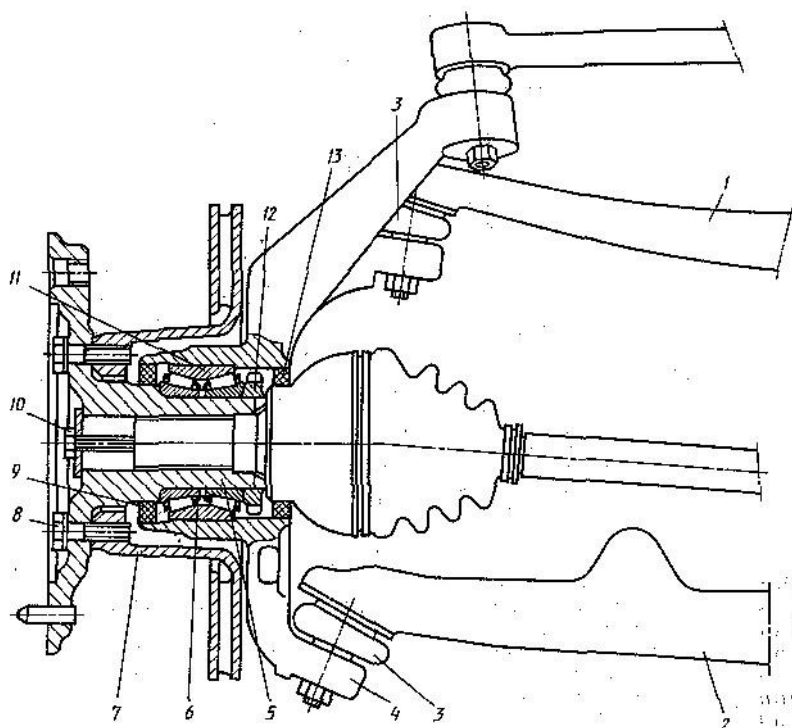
Передняя подвеска легких грузовиков C32/C35 фирмы «Ситроен» с двумя поперечными рычагами 1 и 2 и шарнирами 3, соединяющими эти рычаги с опорой 4 подшипника колеса. Двухрядный конический роликовый подшипник 6 сидит на ступице 5, в которую посредством болта 10 втягивается разгруженный от изгиба вал колеса. Болты 8 крепят вентилируемый тормозной диск 7 с внутренней стороны к ступице 5 колеса. Чтобы иметь небольшие напряжения на дисковом колесе, ступица имеет большой наружный диаметр
